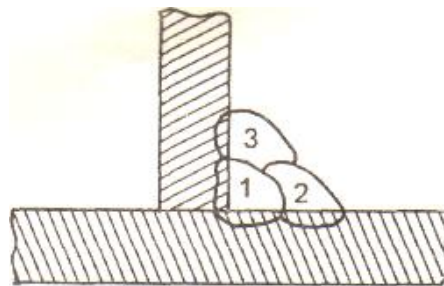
Aplicación del segundo cordón de soldadura.
